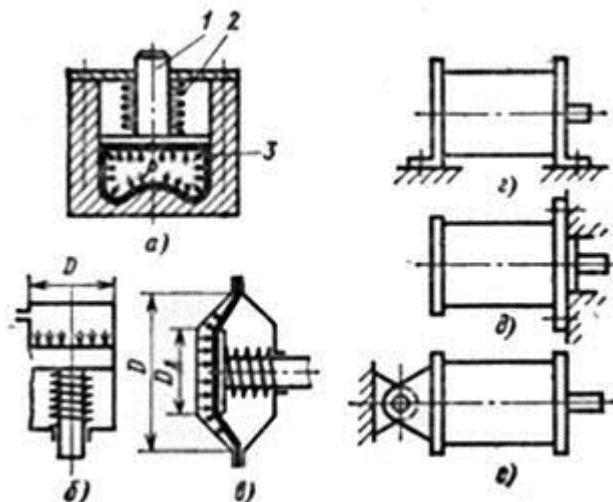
Схемы пневмодвигателей одностороннего действия и способы крепления на корпусе
